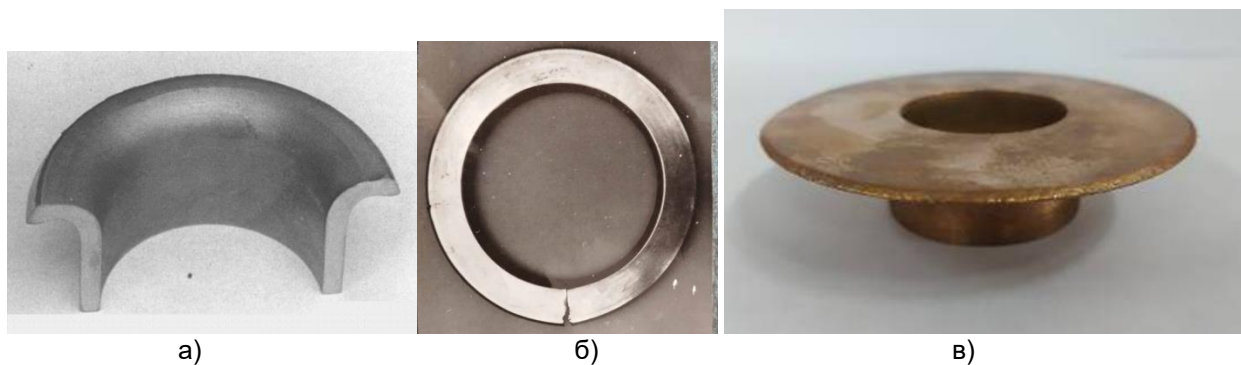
Заготовки, що відбортовувалися методом ШО: а – проміжна стадія, б – руйнування заготовки зі сталі 30ХГСА, в – відбортована заготовка із міді М06
